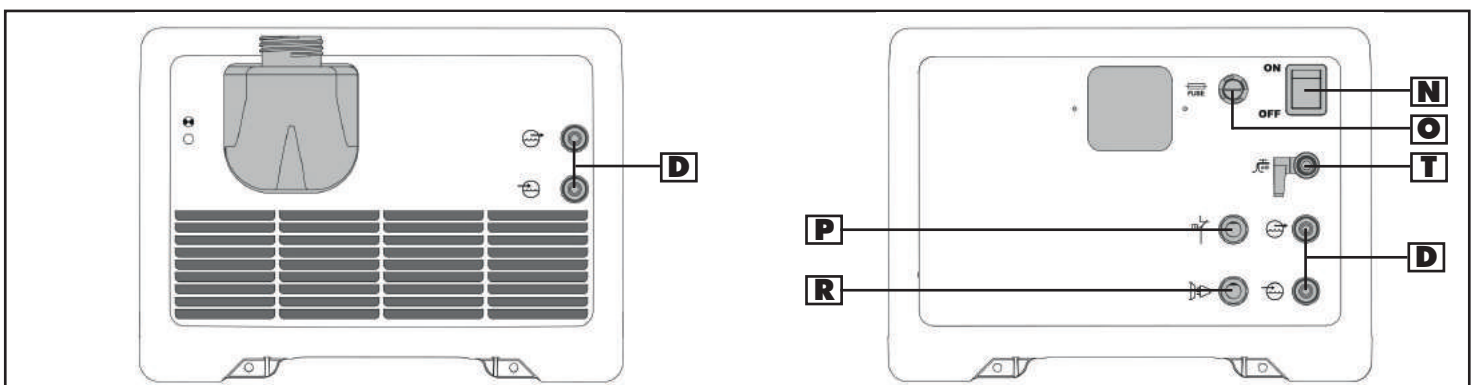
Unitè refroidissement par eau - vue avant et arrière
